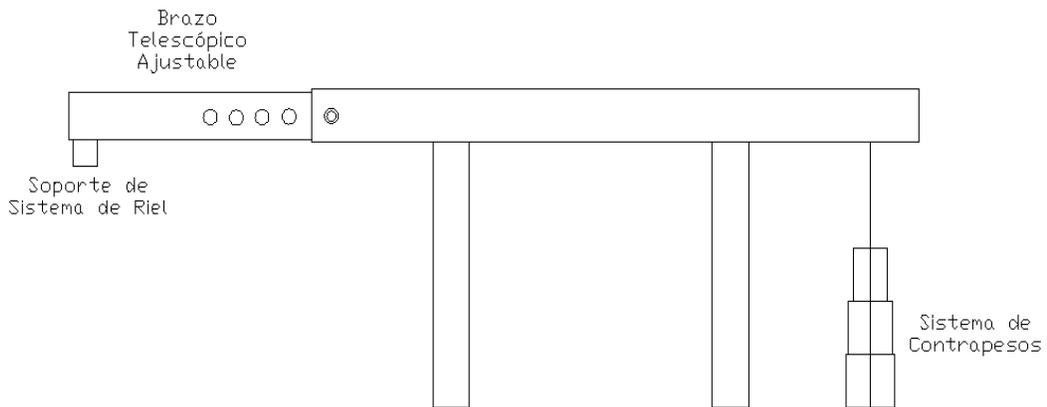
Sistema Viga Caballete para Instalación de Módulos
